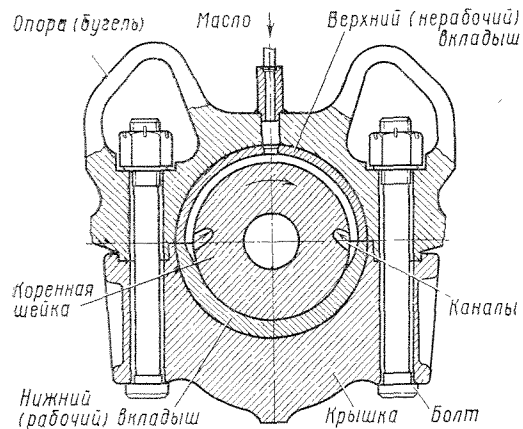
Опора коренного подшипника нижнего коленчатого вала дизелей 10Д100, 2Д100
